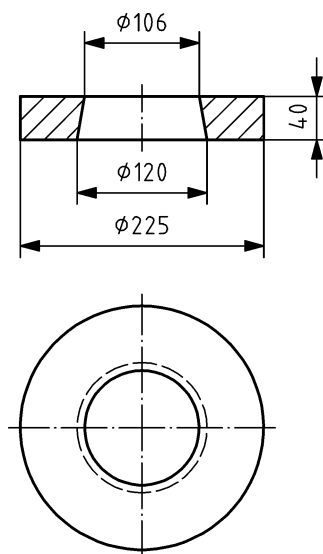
Beispiel für die Maße einer mit Stahl beschwerten Manschette
